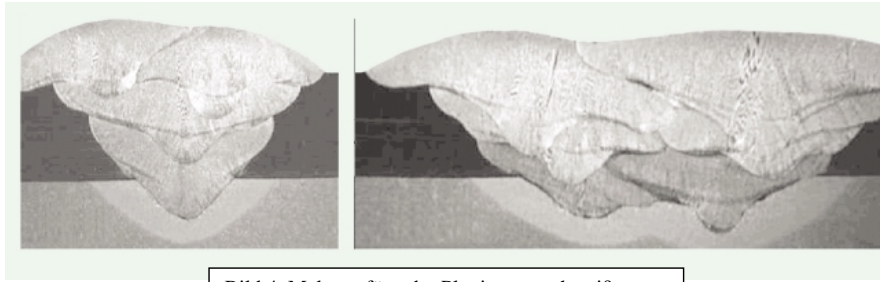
Makrogefüge der Plattierungsschweißungen
